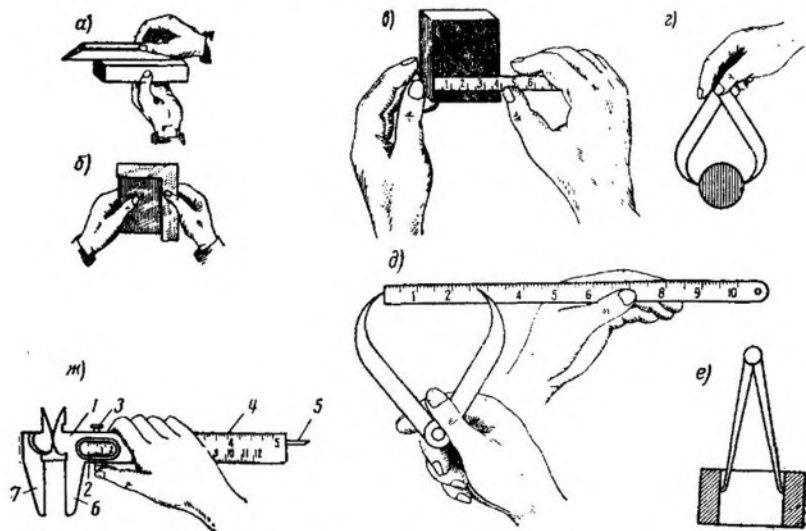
Приемы проверки обрабатываемых поверхностей и пользования измерительным инструментом
